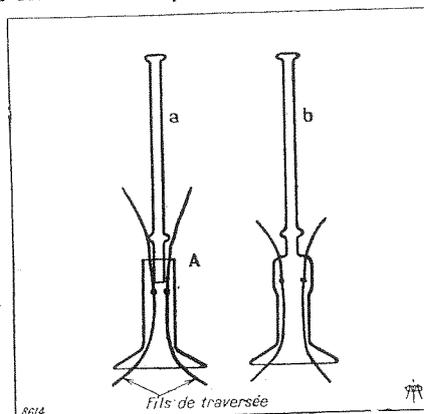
Schéma des éléments du pied, assemblés (en a) et réunis définitivement par soudure (en b).
